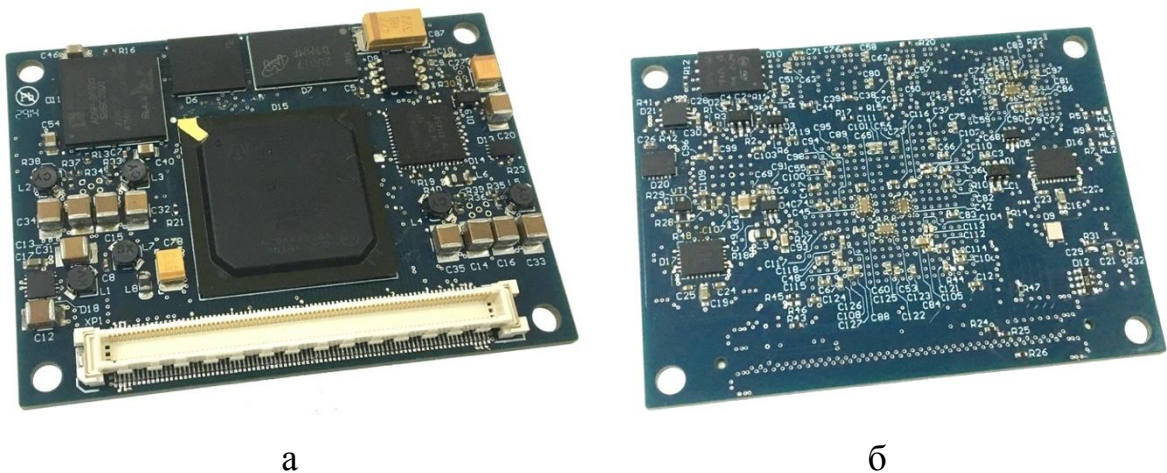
Внешний вид платы ERCS: а) вид сверху; б) вид снизу
